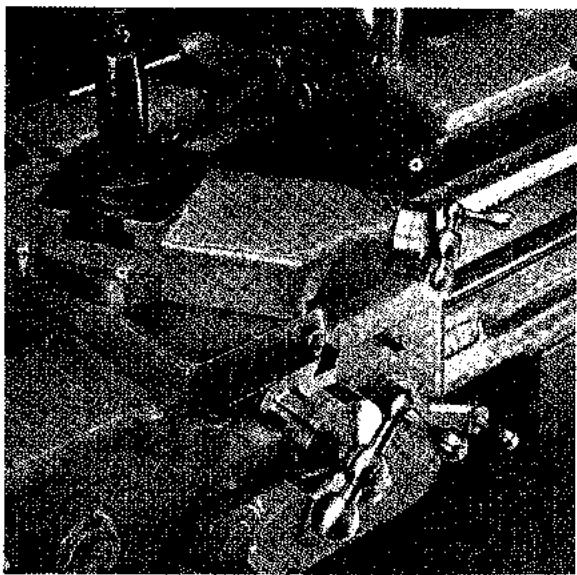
Soporte orientable (South Bend Lathe Works).
